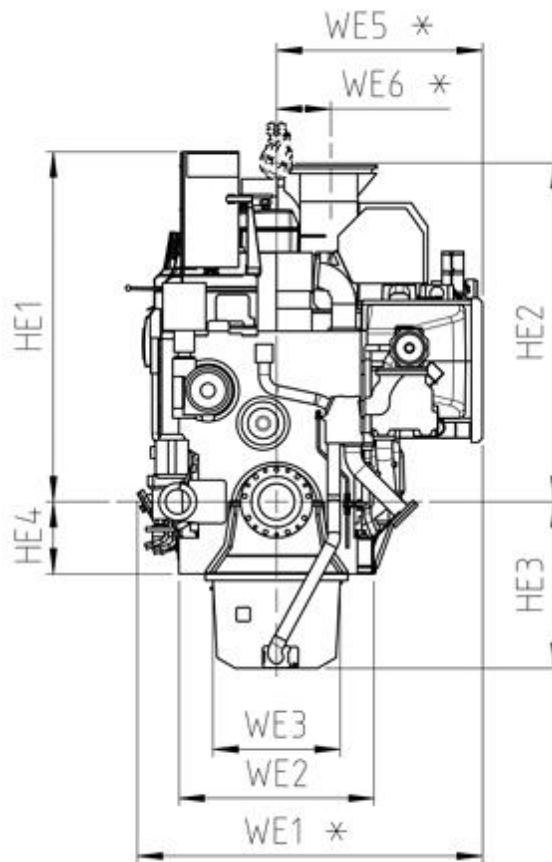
Dimensiones del motor Wärtsila 32 metanol en vista de alzado.
